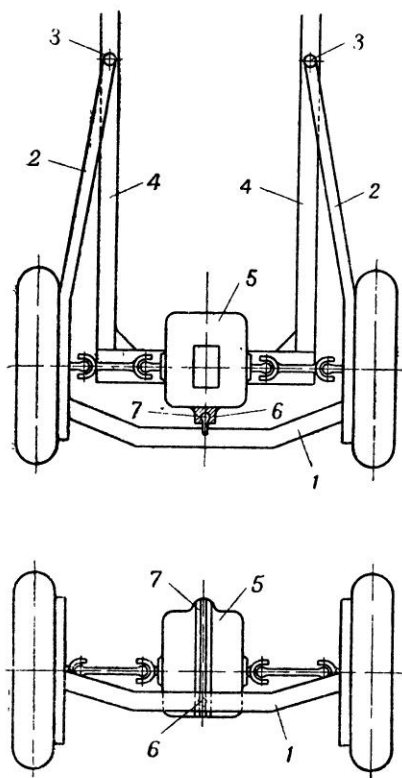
Схема задней подвески с неизменной шириной колеи задних колес и направляющей на картере главной передачи
